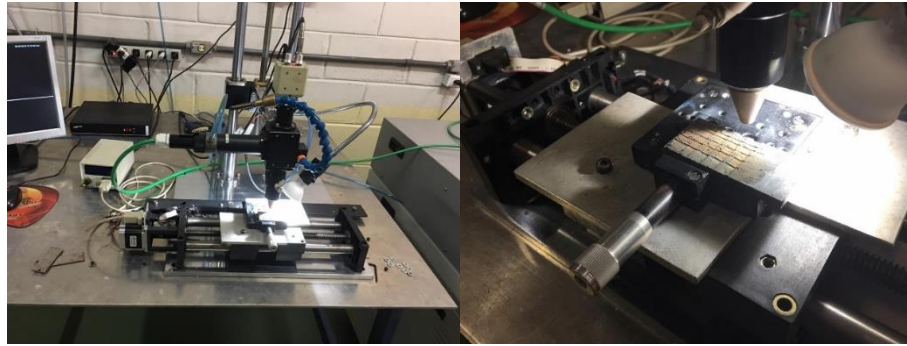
Cabeçote de Soldagem [Elaborado pelo Autor].
